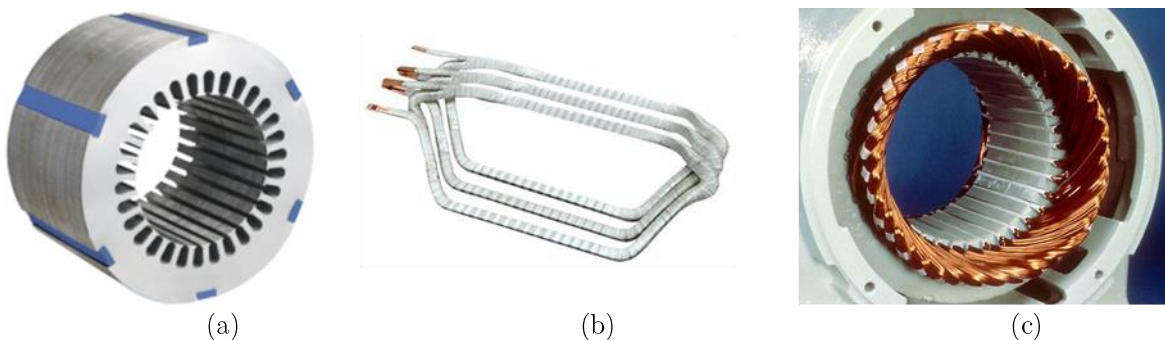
Stator d'une machine électrique, (a) circuit magnétique [4], (b) bobines [5], (c) stator complet [6]
